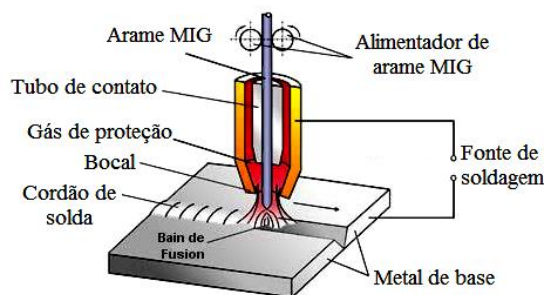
Esquema ilustrativo da soldagem MIG/MAG (http://epa.soudage.free.fr/tig/procede_mig.JPG).
